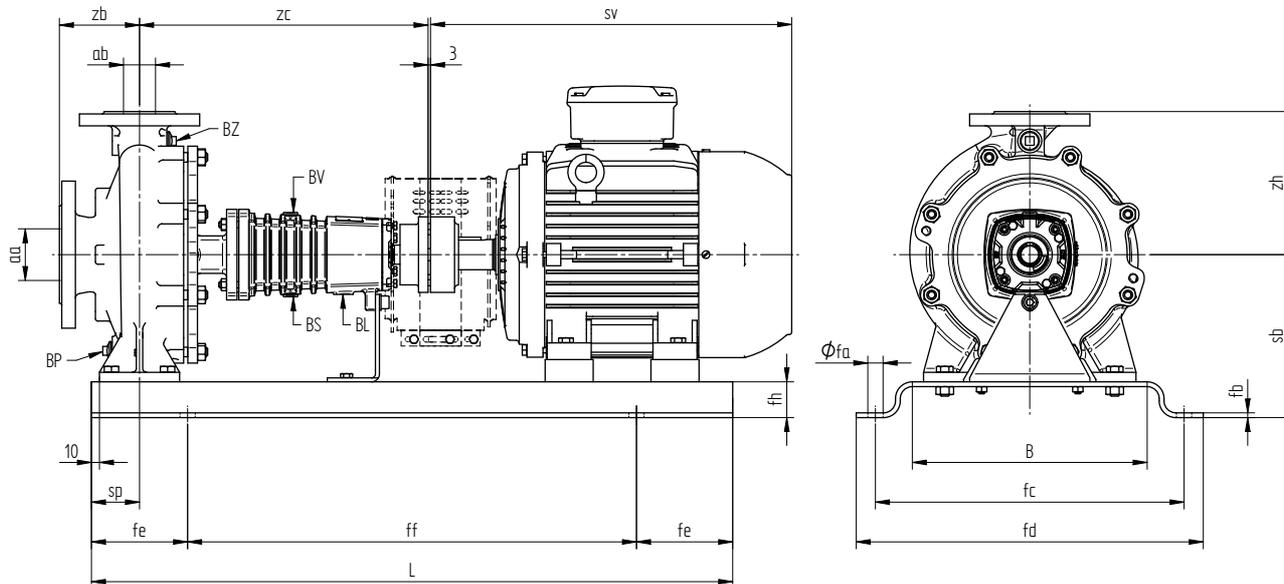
Unidad del motor de la bomba con acoplamiento estándar.
